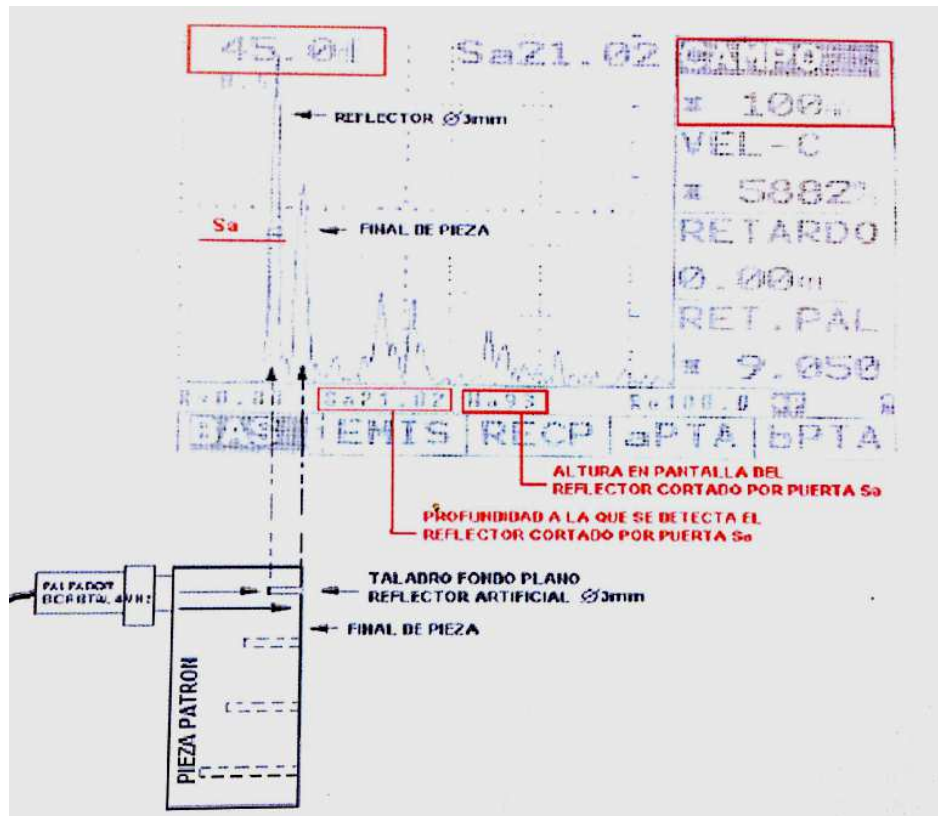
Reflector de $\varnothing 3\text{mm}$ a 21 mm de profundidad
